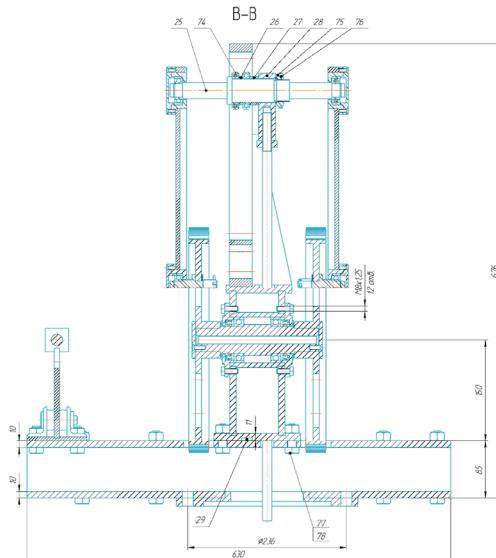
Сборочный чертеж силовой головки (вертикальный разрез по оси вала ветрового колеса
